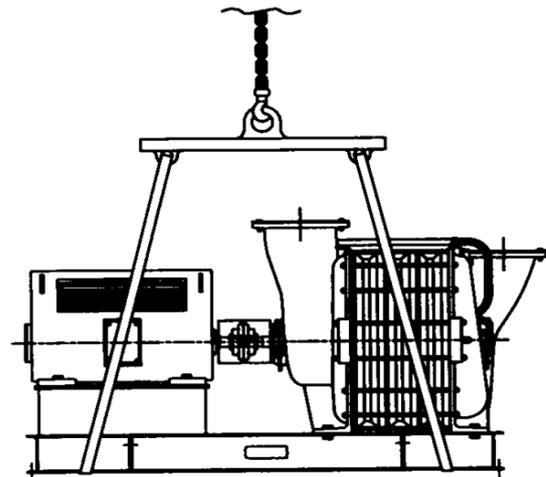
Fissare il mezzo di sollevamento alla struttura in acciaio del gruppo macchina
